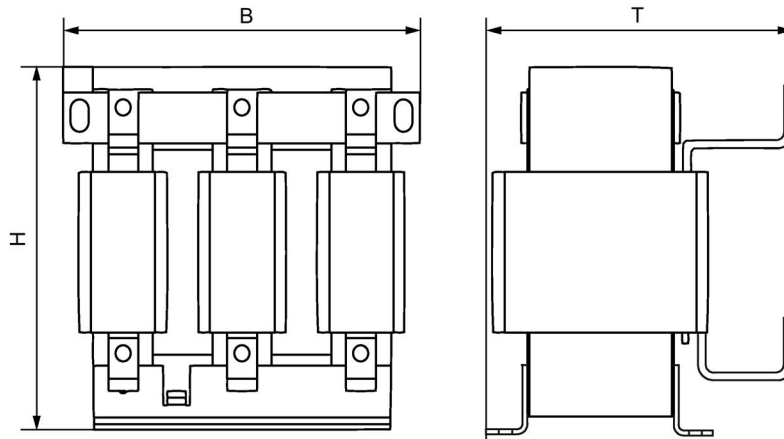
Croquis acotado bobina de motor 6SL3000-2....-AA0, Typ1, para dimensiones ver tabla siguiente
